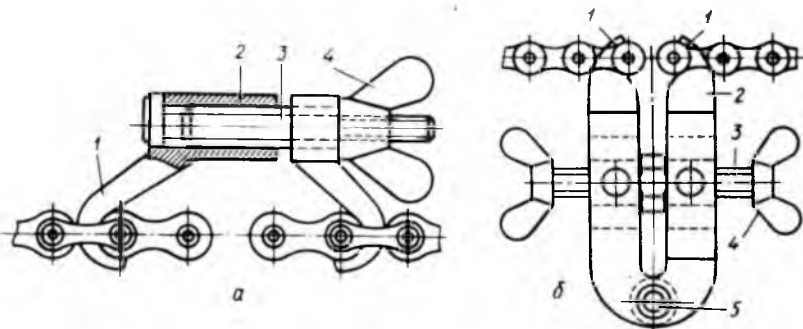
Приспособление для стягивания втулочно-роликовых цепей при разъединении и соединении:
